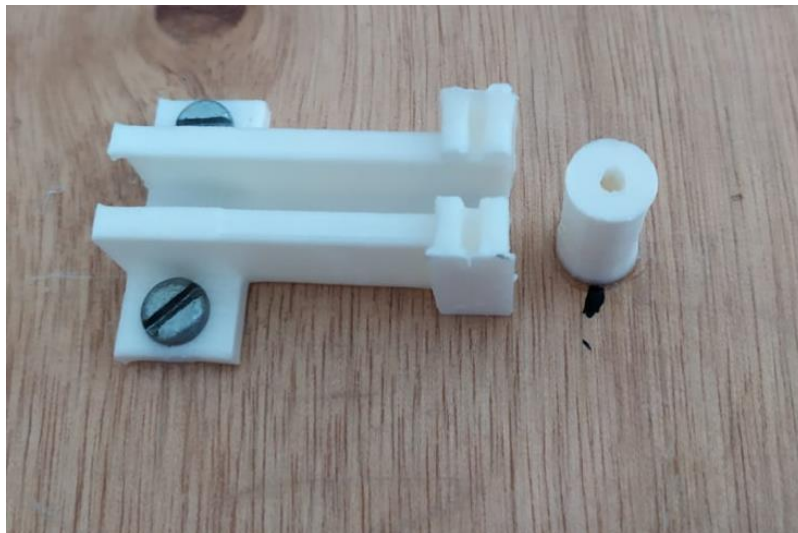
Barra deslizante com suporte + ímãs + ponta metálica
